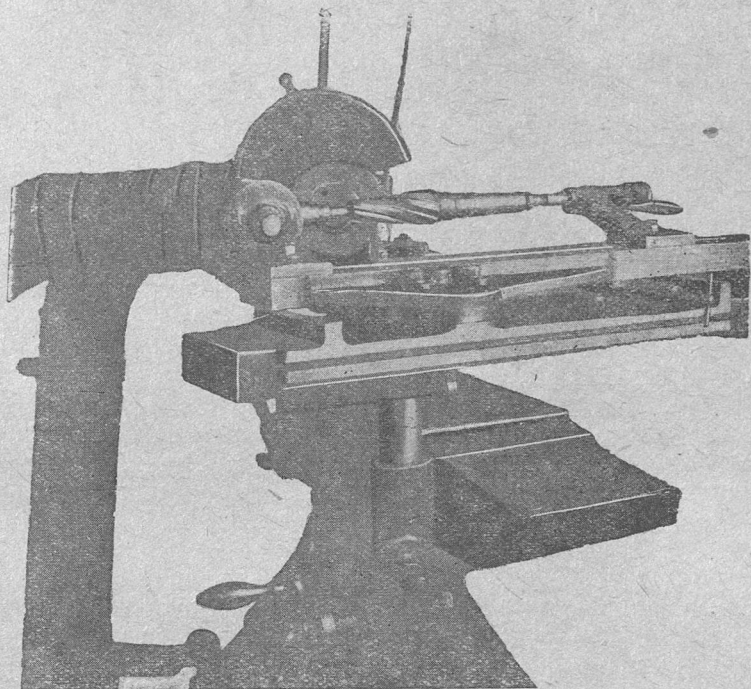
Заточка конусной фрезы на станке завода им. Свердлова.
